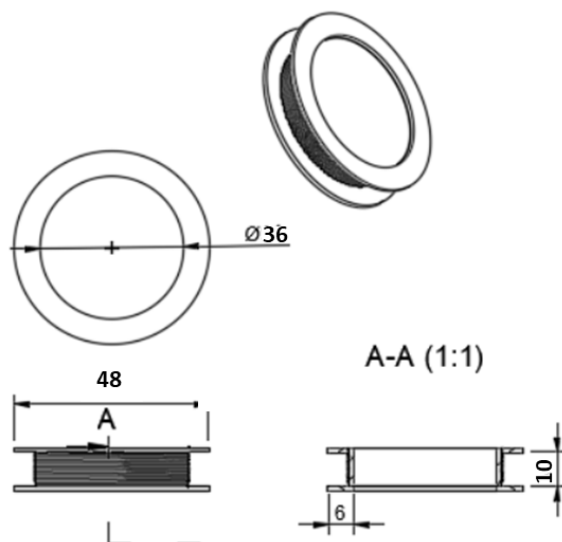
Dimensões do suporte da bobina, unidades em mm.
